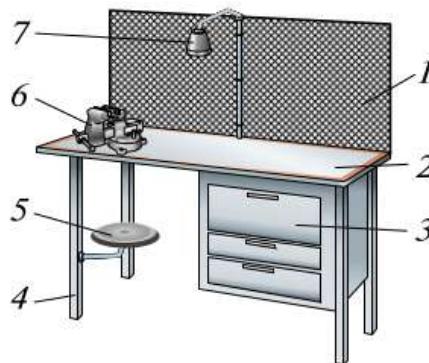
Слесарный верстак: 1 — защитный экран; 2 — столешница; 3 — ящик; 4 — каркас; 5 — сиденье; 6 — слесарные тиски; 7 — светильник
